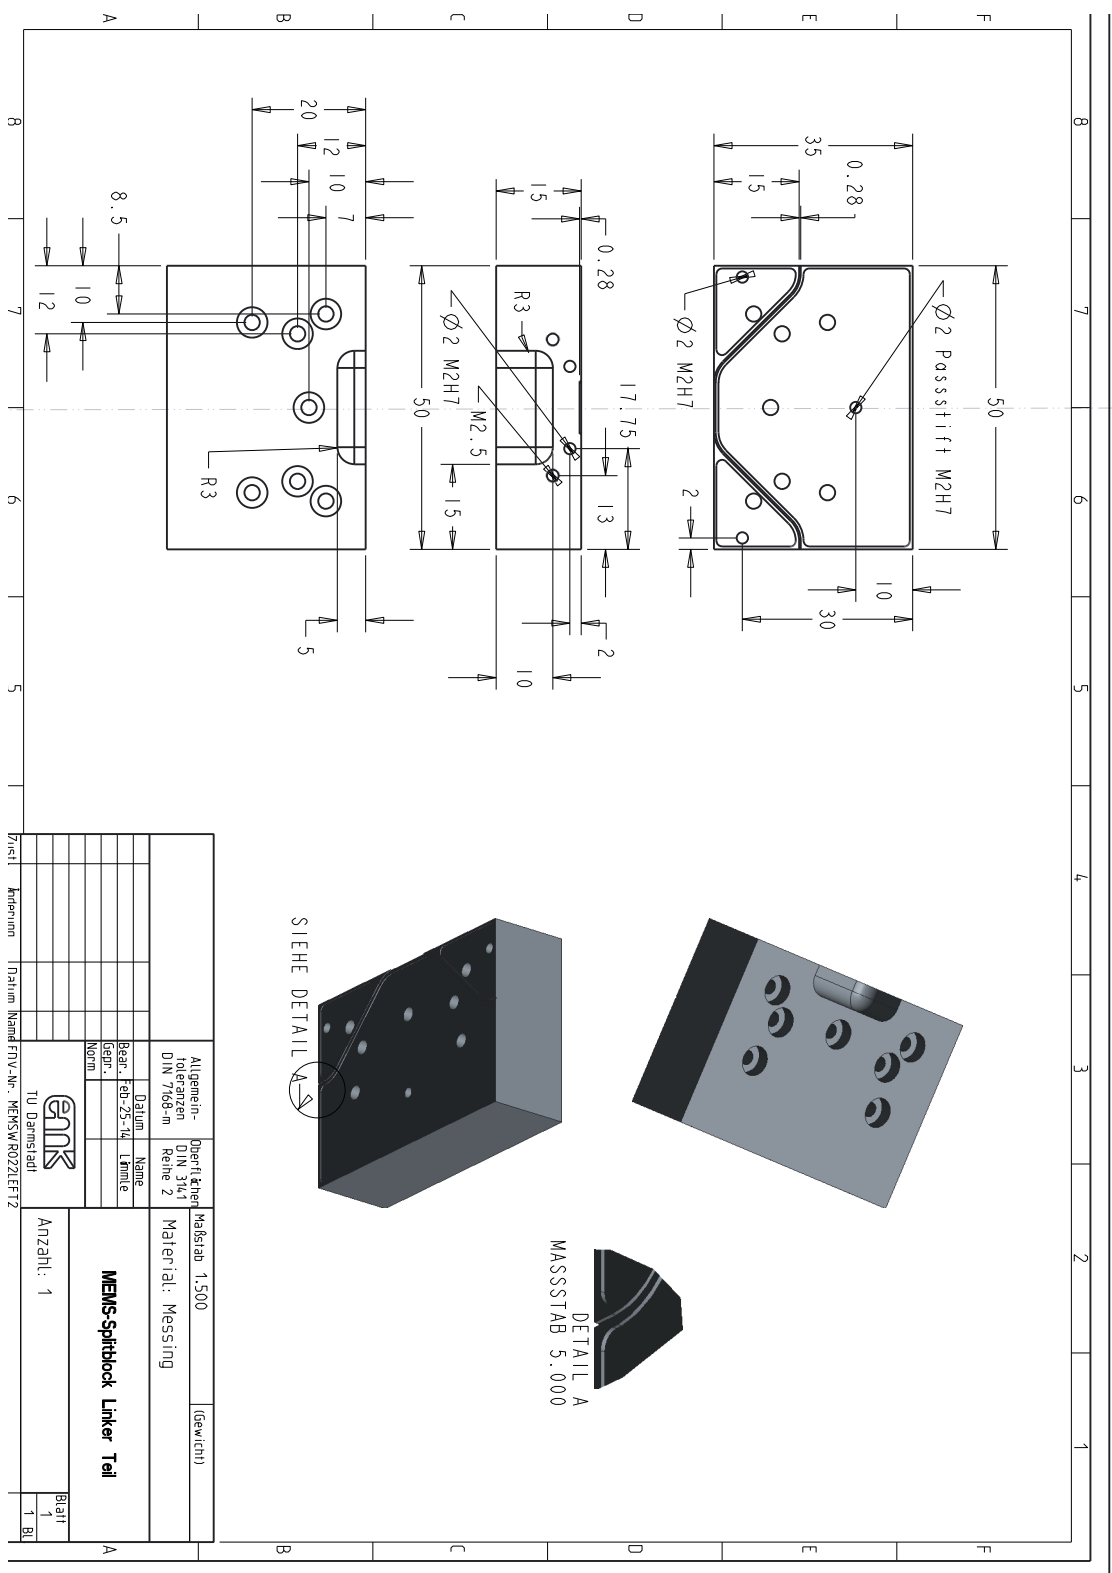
Technische Zeichnung des Splitblocks - 1. Version, linker Teil
